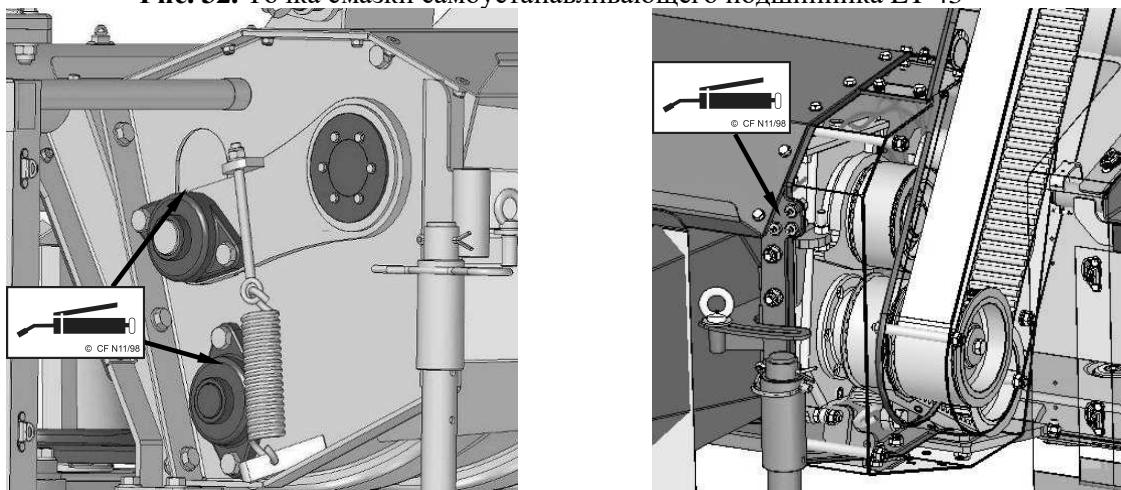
Точка смазки самоустанавливающих подшипников LT 43
